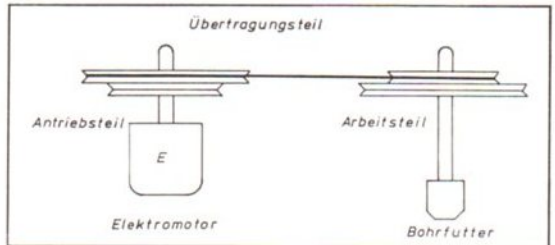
Prinzipskizze einer Tischständerbohrmaschine
